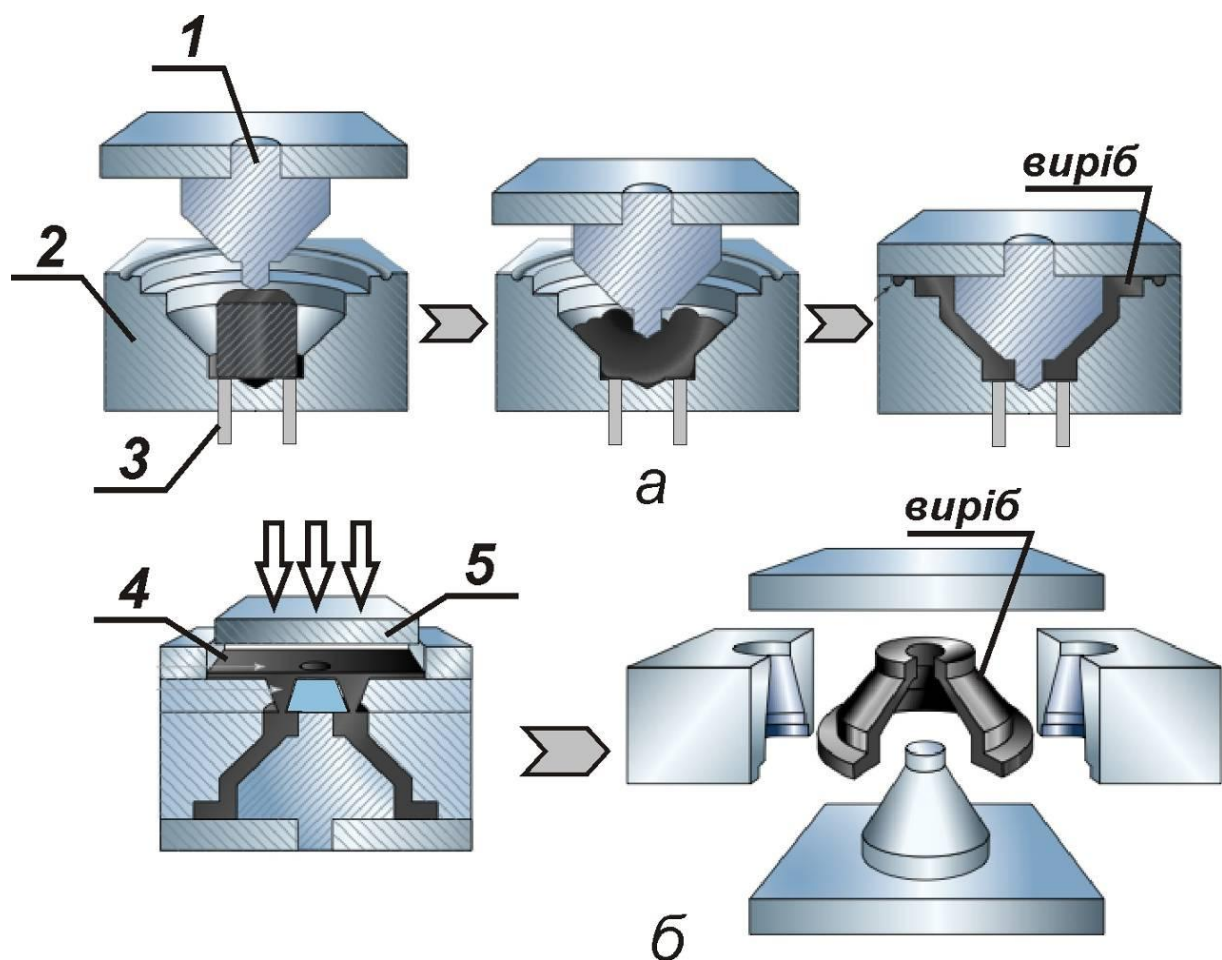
Схема прямого (а) і литтєвого (б) пресування заготовок з пластмас:
